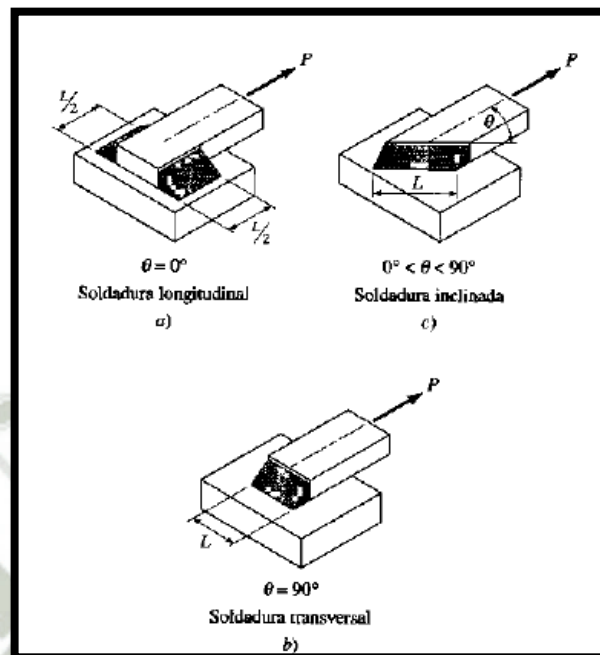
Ángulo de Soldadura longitudinal, transversal e inclinada.
